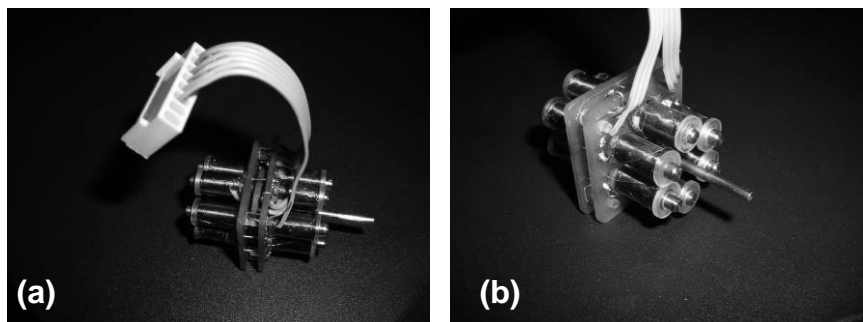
(a) y (b) Vistas del motor listo para su montaje en el módulo.
